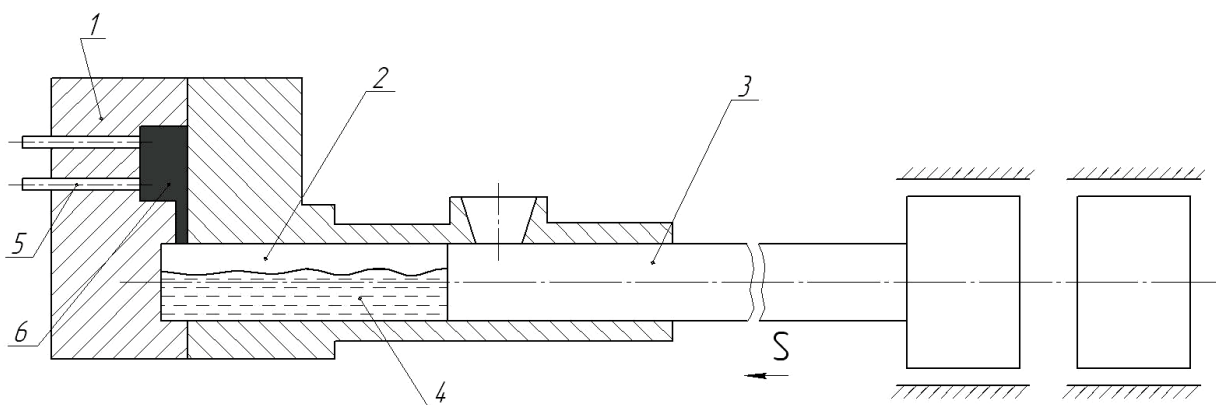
Схема холодної горизонтальної камери пресування: 1 – прес-форма; 2 – камера пресування; 3 – поршень; 4 – розплав; 5 – виштовхувачі виливків; 6 – виливок [1]
